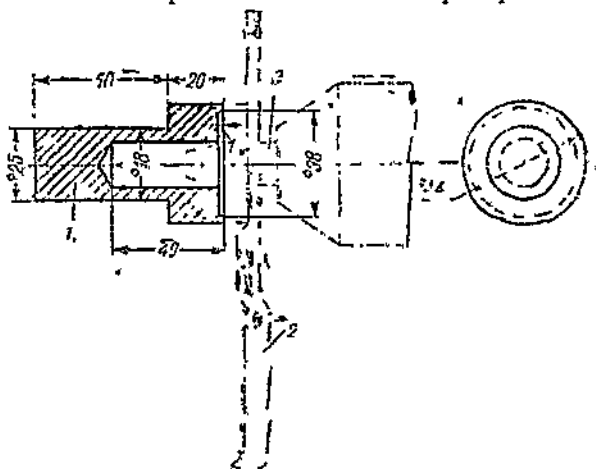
Оправка для насадки подшипниковых колец для ГБТ и ГБФ:
